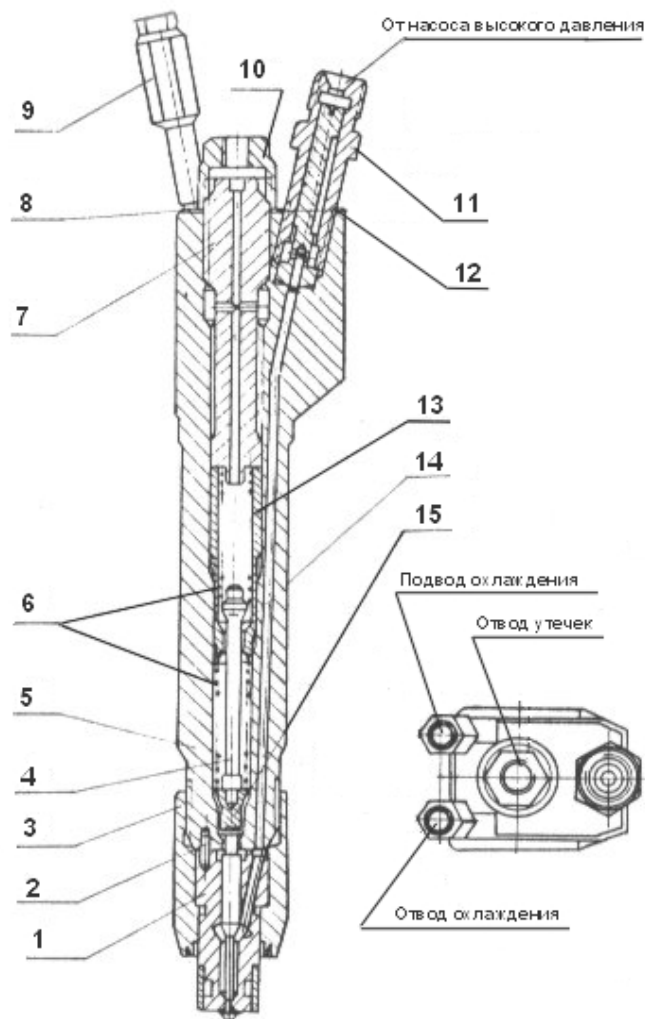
Форсунка: 1 – розпилювач; 2 – штифт 3x12; 3 – ковпак нажимний; 4 – штовхач; 5 – корпус форсунки; 6 – пружини; 7 – гвинт регулювальний; 8 – прокладка мідна; 9 – штуцер; 10 – контргайка; 11 – фільтр щільовий; 12 – прокладка; 13 – гильза; 14 – стержень штовхача; 15 – тарілка
